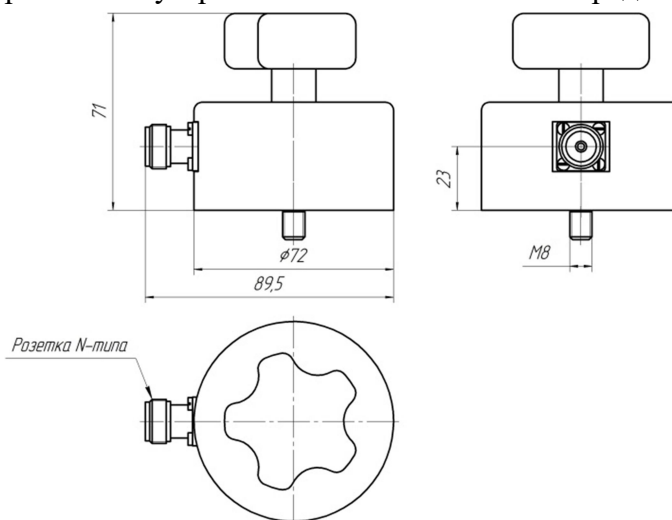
Общий вид калибровочного устройства КНПР. 411135.002
